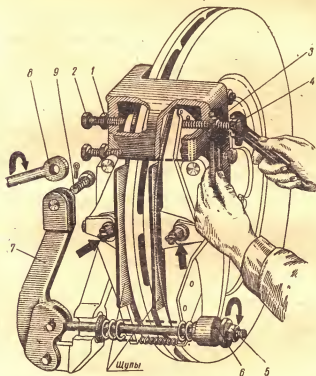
Регулировка ручного тормоза автомобиля ЗИЛ-164:
